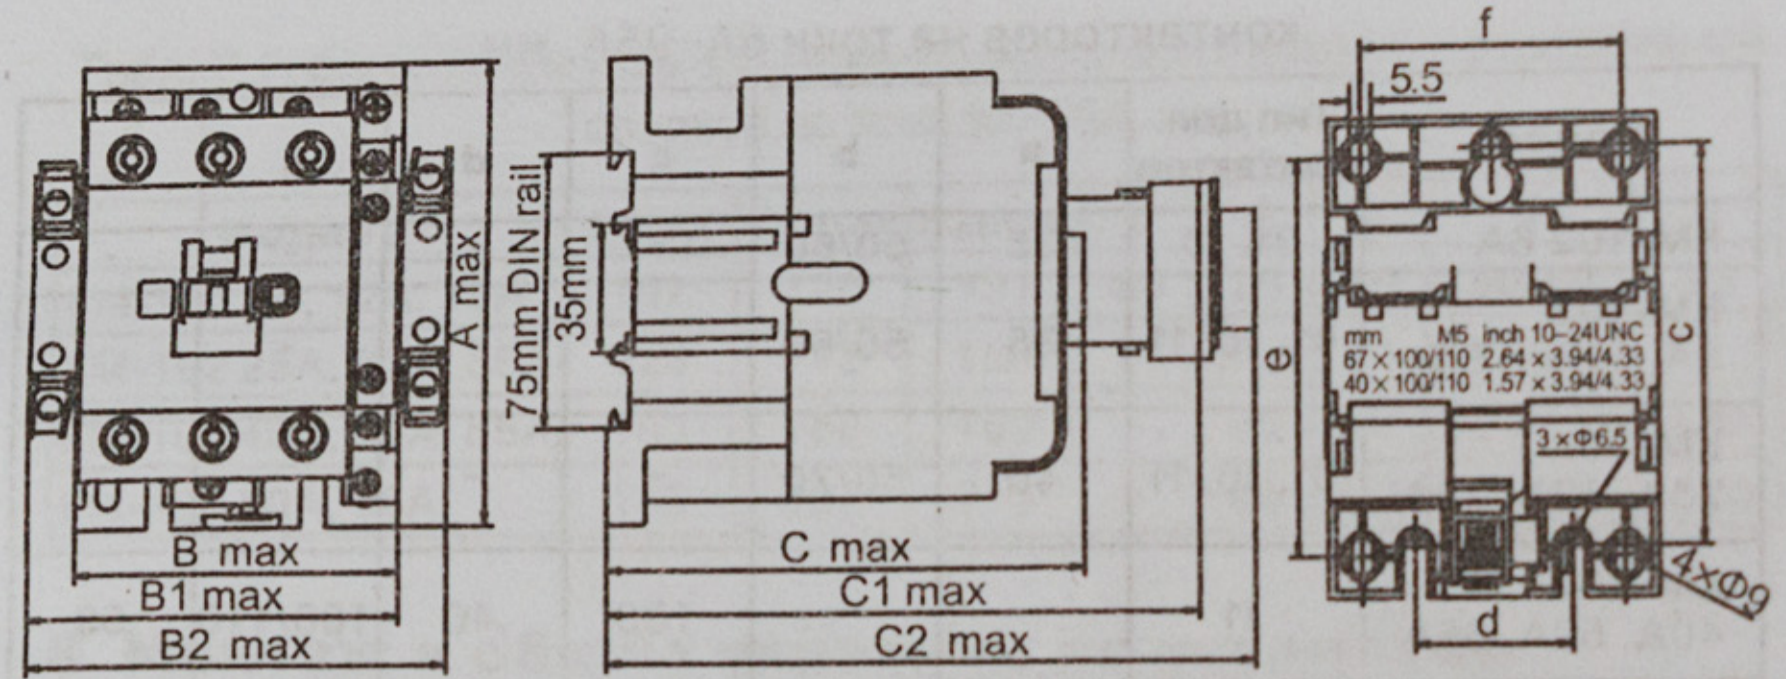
Габаритные и установочные размеры контакторов на токи 40А-95А, мм.
